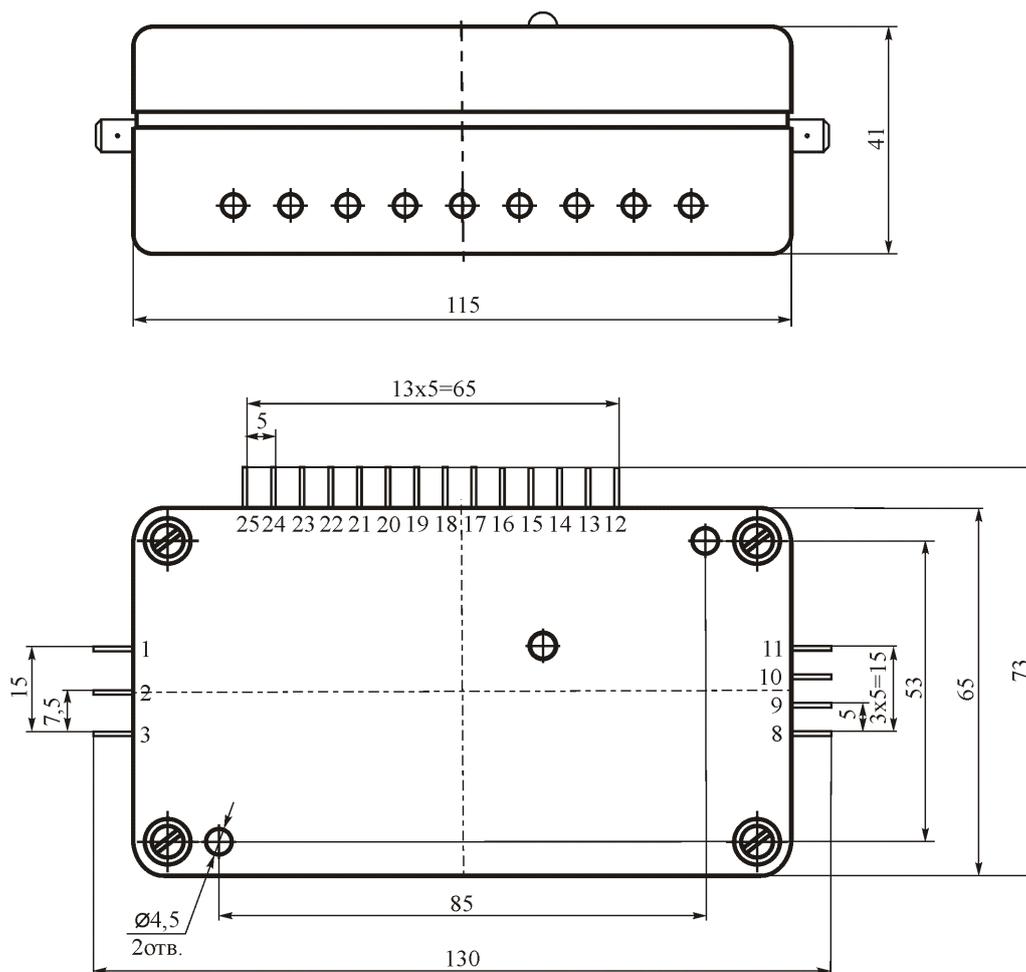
Габаритный чертеж ДТРМ-НК
